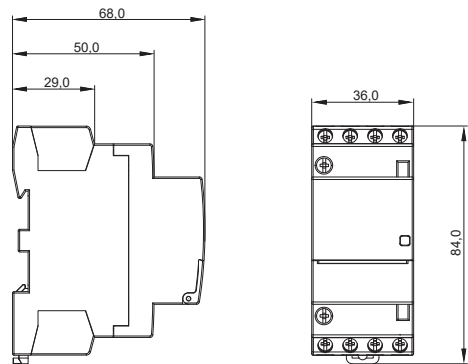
Габаритные размеры контакторов до 25 А, 4P / Figure 2 – Overall dimensions of contactors up to 25 A, 4P
